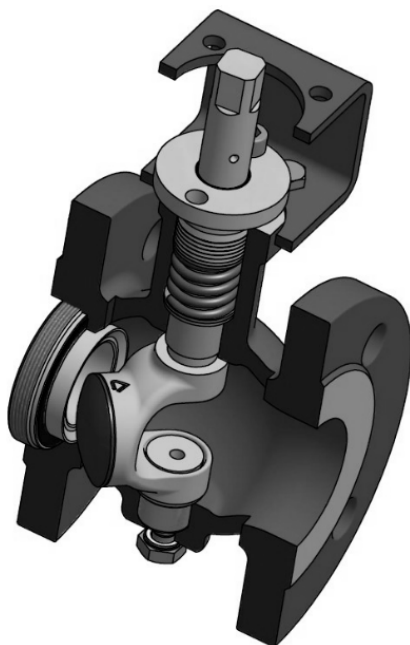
Schéma d'assemblage pour vanne type 62.7
